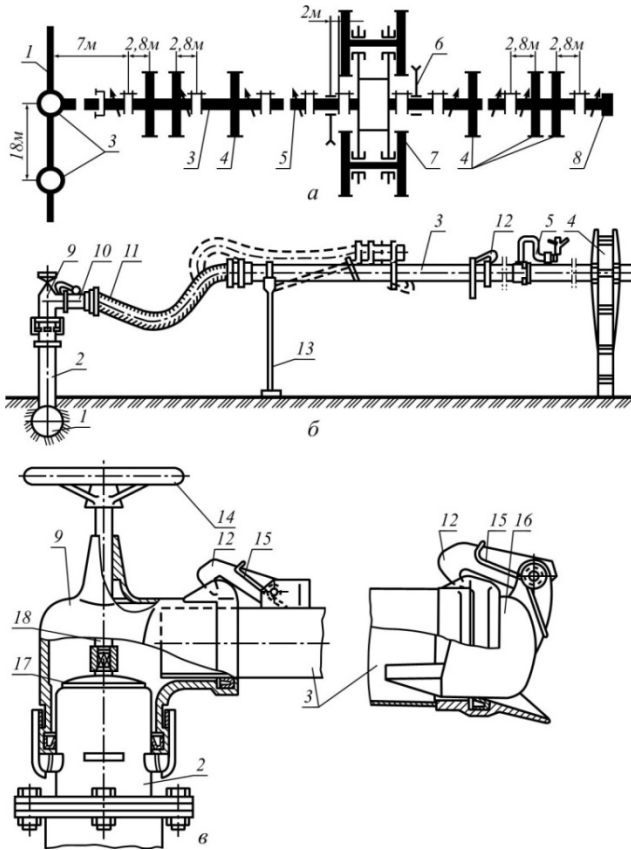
Крило дощувального трубопроводу «Волжанка»: а – монтажна схема; б – пристрій вузла приєднання; в – вузли кінцевих патрубків; 1 – закритий водовідвідний трубопровід; 2 – гідрант; 3 – трубопровід (секція); 4 – опорне колесо; 5 – дощувальний апарат; 6 – протівітрове гальмо; 7 – привідний візок; 8 – заглушка; 9 – колонка; 10 – патрубок; 11 – гнучкий шланг; 12 – гачок; 13 – опора; 14 – маховик; 15 – пружина; 16 – заглушка; 17 – клапан гідранта; 18 – ключ
